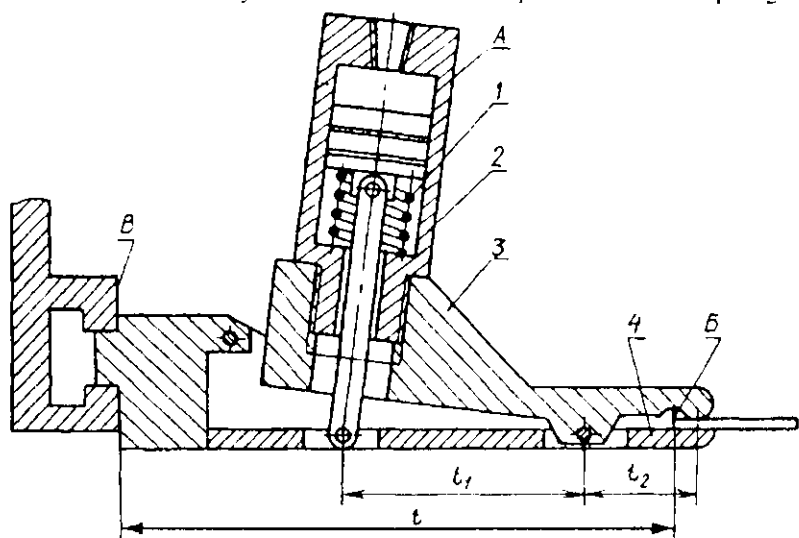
Схема пневматического зажима заготовки дыропробивного пресса модели К0136Б
